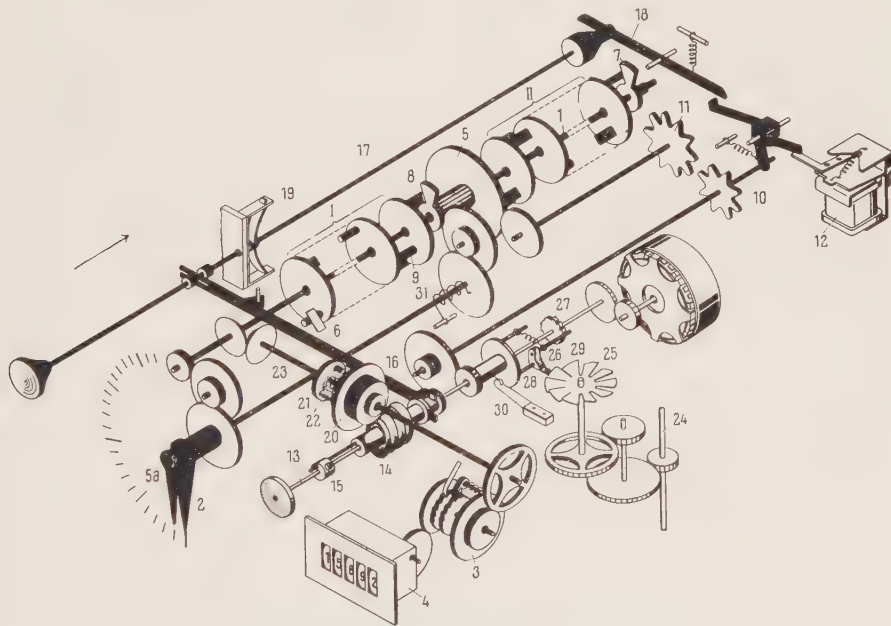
Dispositivo dell'indicatore di massima del contatore di fig. 4.
